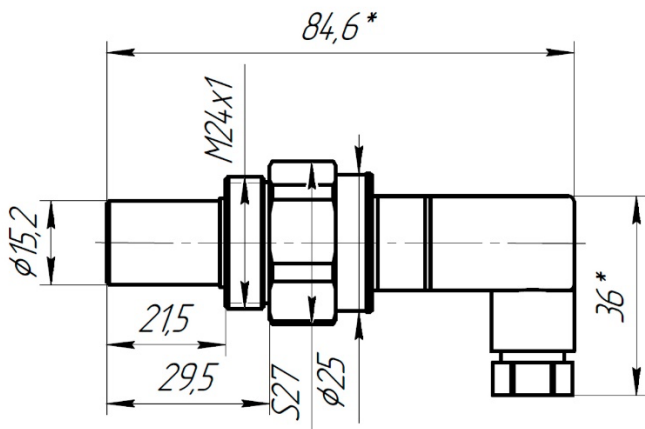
Установочные и габаритные размеры преобразователя ДТР-4.
